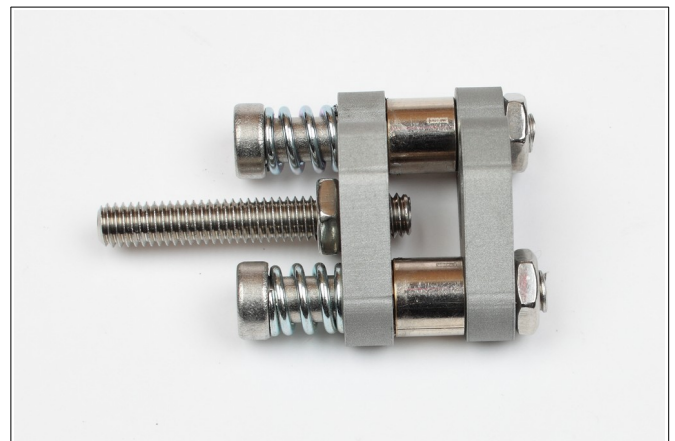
Die Schrauben werden mit 3 Umdrehungen gelöst (M6 hat eine Steigung von 1 mm), und dann in dieser Stellung mit den Kontermuttern gesichert.
